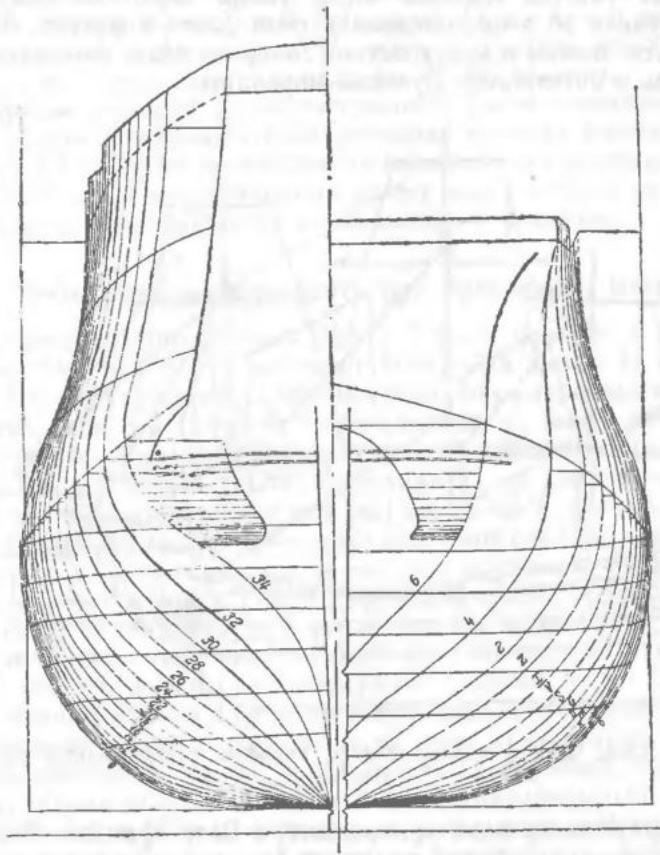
а. Теоретический корпус 100-пушечного корабля, утвержденный лично Петром I.
